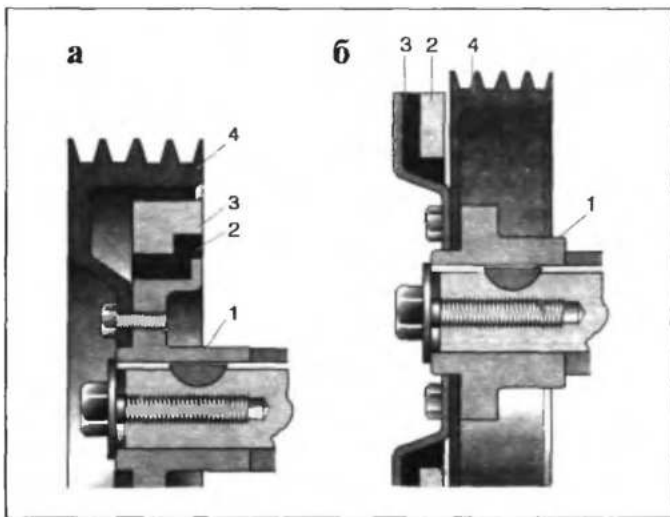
Демпферы крутильных колебаний: а — внутри шкива; б — снаружи; 1 — ступица; 2 — инерционная масса; 3 — резиновая прокладка; 4 — шкив
